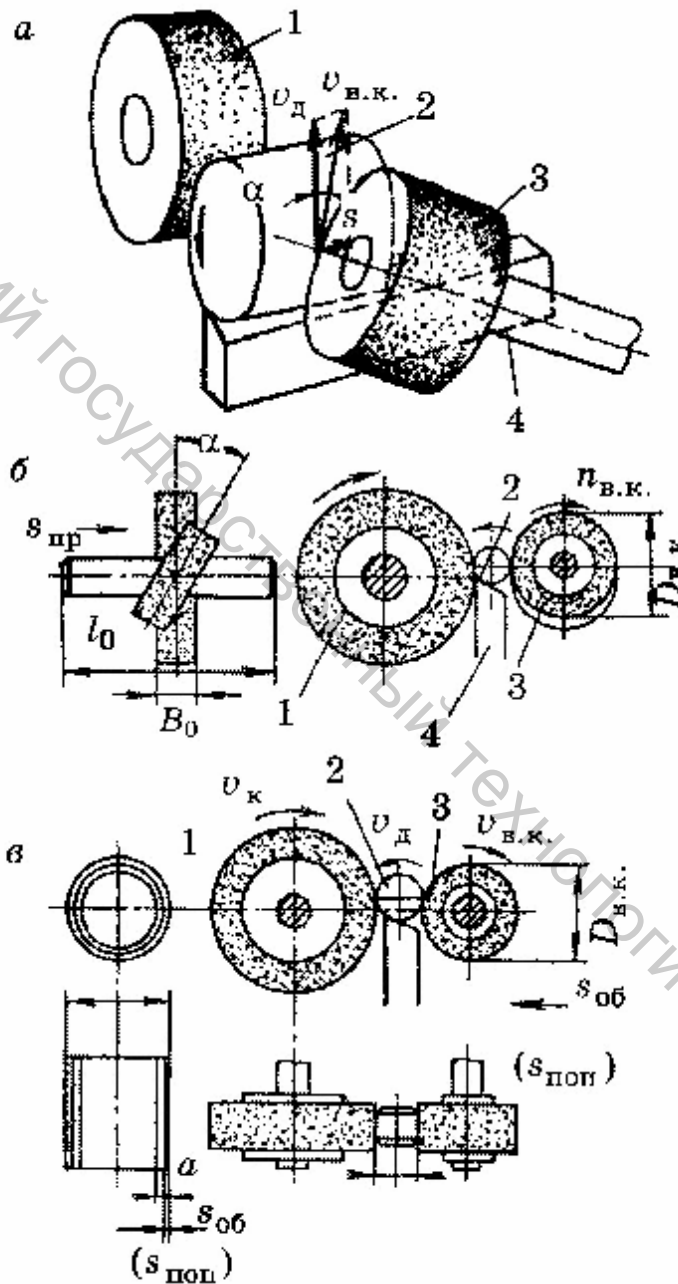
Схемы бесцентрового шлифования: а — общая схема; б — с продольной подачей; в — с поперечной подачей; 1 — шлифовальный круг; 2 — обрабатываемая деталь; 3 — ведущий круг; 4 — опора (нож)
